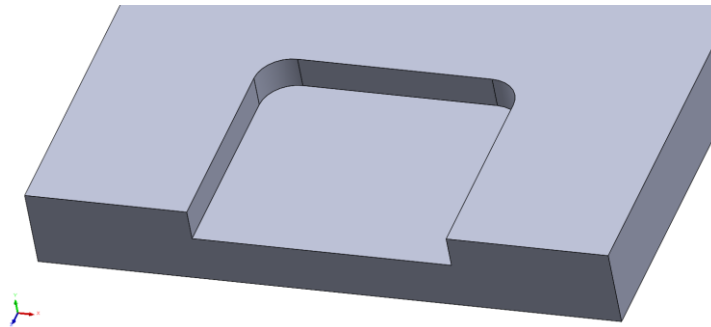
Model obrobku pro otestování funkce AFC [autor]
